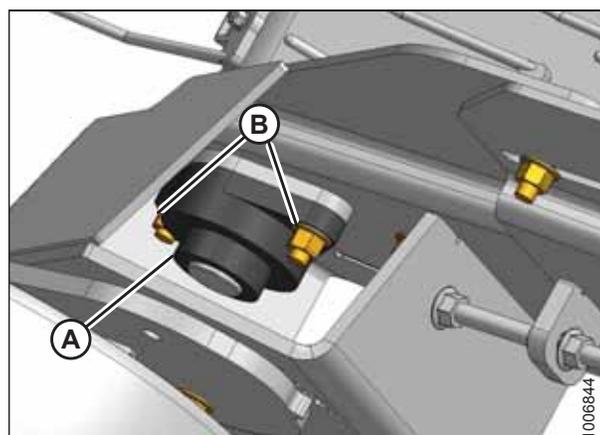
Rodamiento tensor de la plataforma frontal izquierda
